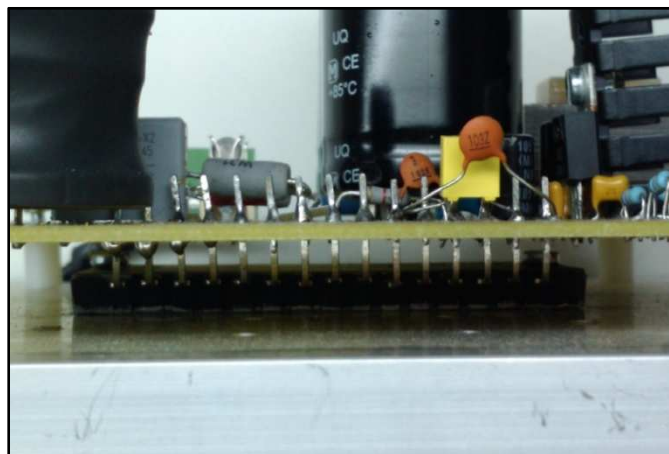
Detall de la soldadura del mòdul de potència
